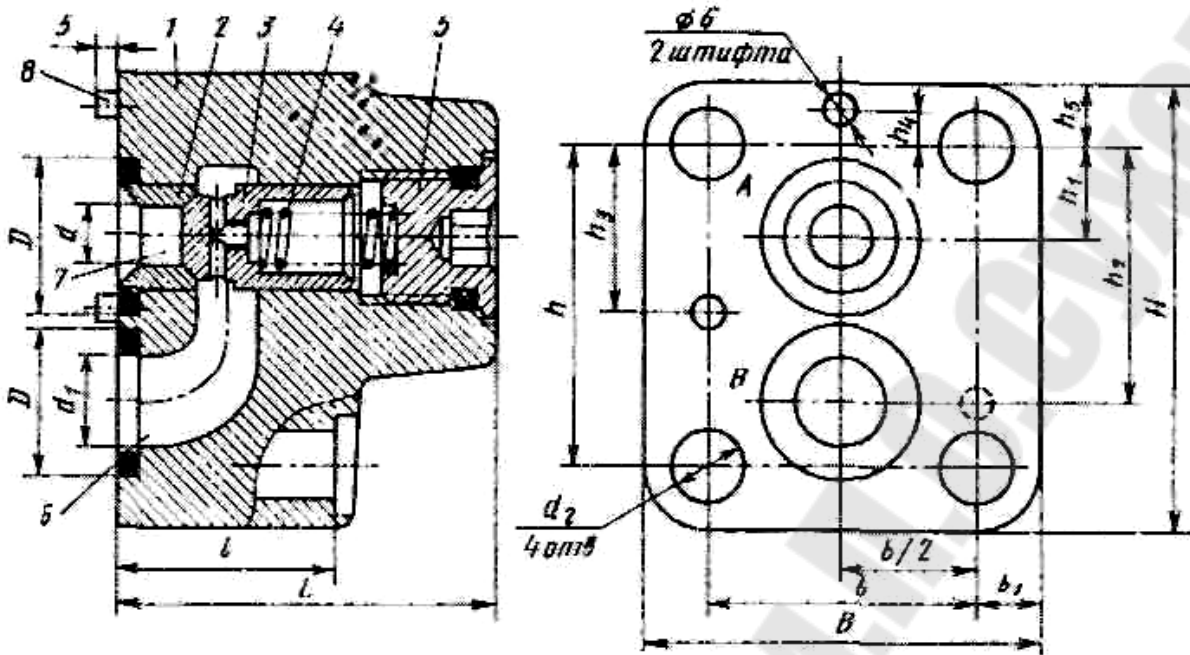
Конструкция, габаритные и присоединительные размеры обратных клапанов стыкового монтажа типа 1МКО
